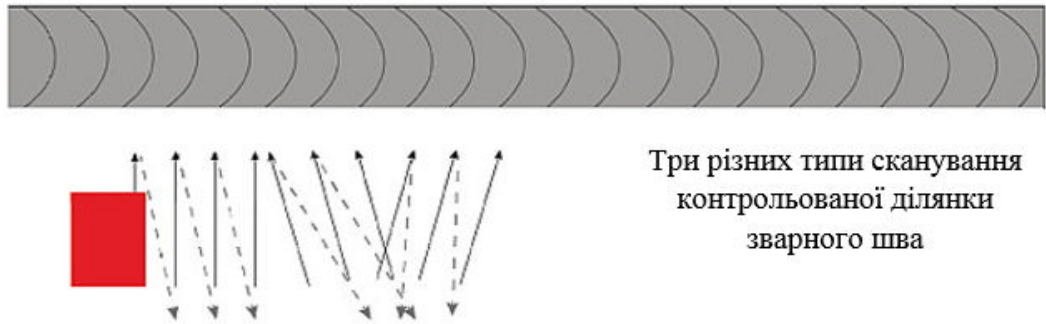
Сканування контрольованої ділянки зварного шва
